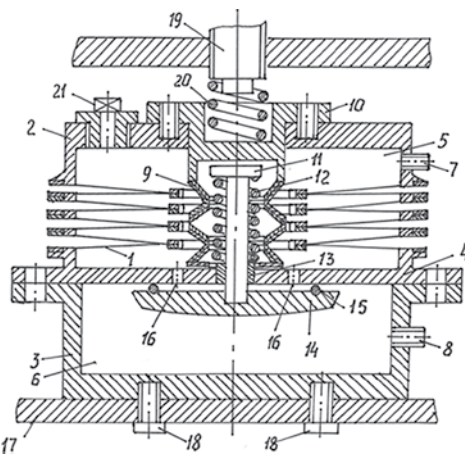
Конструкция металлопневматического амортизатора (тип АМПА)
